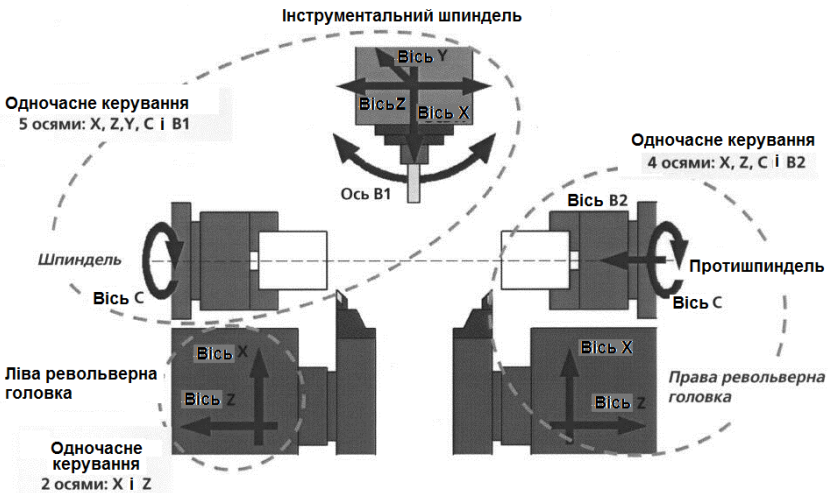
Схема розміщення вузлів верстата Super NTX
